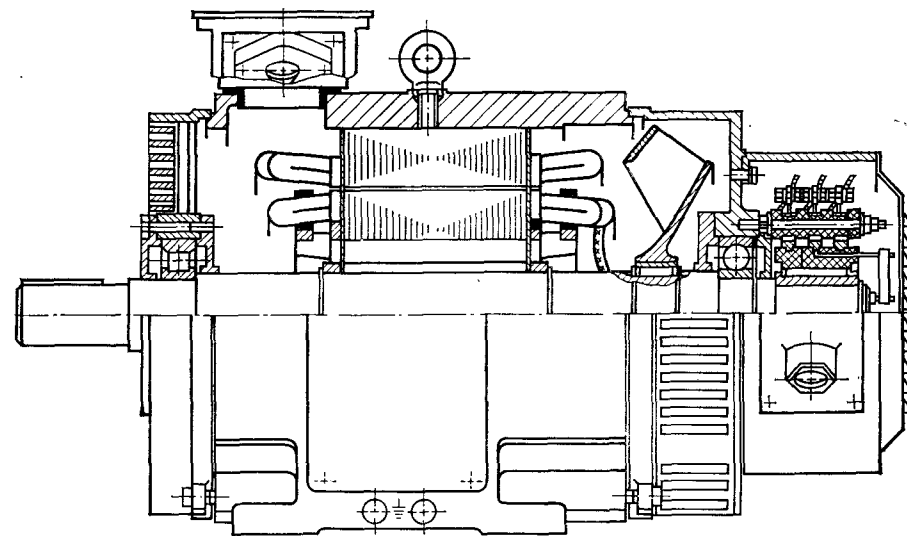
Асинхронный двигатель с фазным ротором 4АНК200, степень защиты IP23
